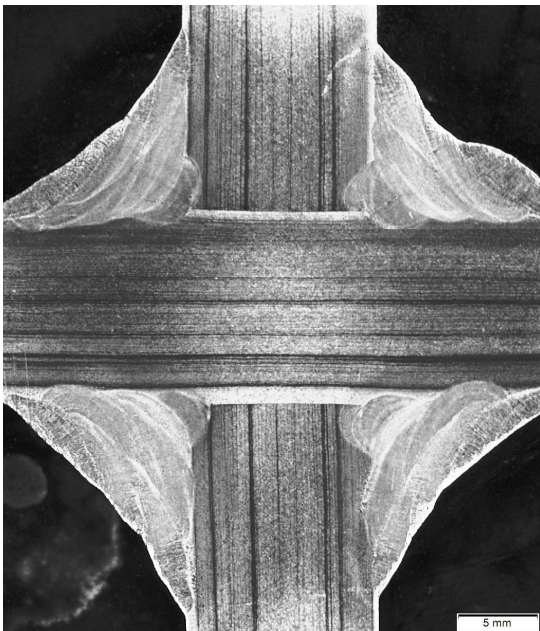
Probe G03-03, Schweißnaht FAT 112, Riss in der Schweißnaht, Vergrößerung
